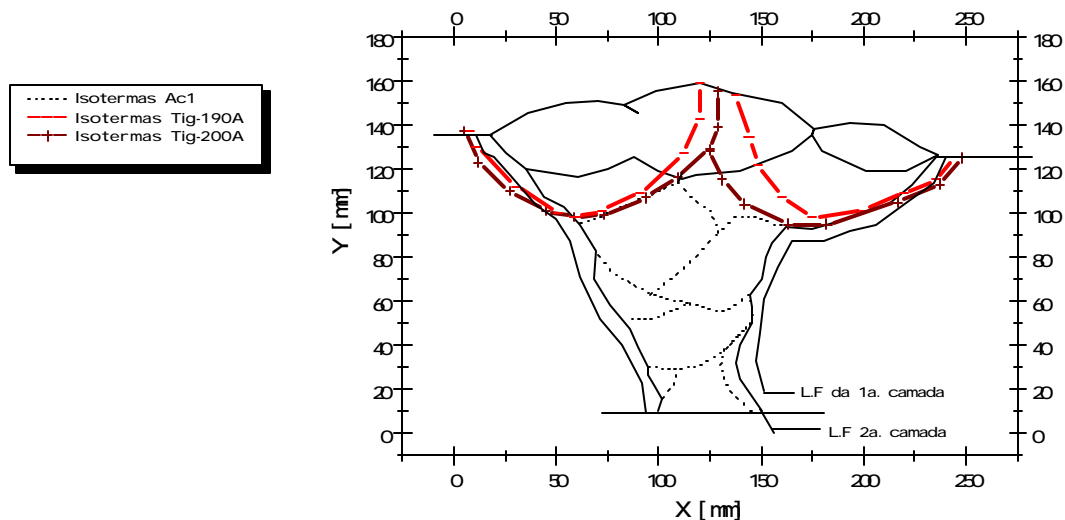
Perfil da junta soldada com chanfro em V.
